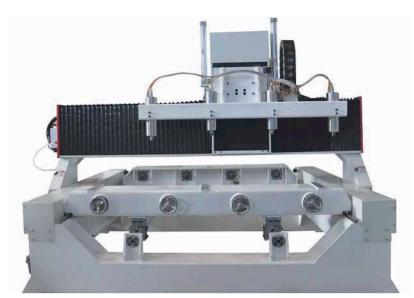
Фрезерно-копировальный станок Beaver-1300
